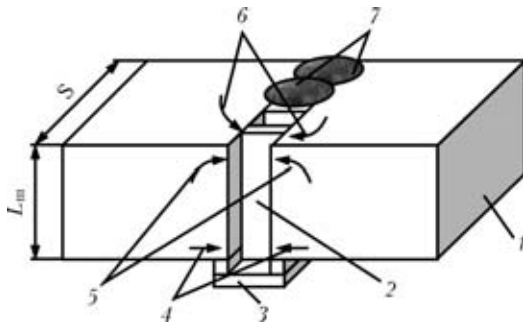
Схема ожидаемых деформаций деталей при МЭШС: 1 — свариваемая деталь образца; 2 — формирующая перемычка; 3 — входной технологический карман; 4 — поперечная усадка  $\Delta b$ ; 5 — поворот свариваемых деталей в плоскости стыка  $\beta$ ; 6 — поворот свариваемых деталей в плоскости, перпендикулярной сварному многослойному шву  $\gamma$ ; 7 — выполненные слои сварного шва;  $S$ ,  $L_{ш}$  — толщина и длина сварного стыка
